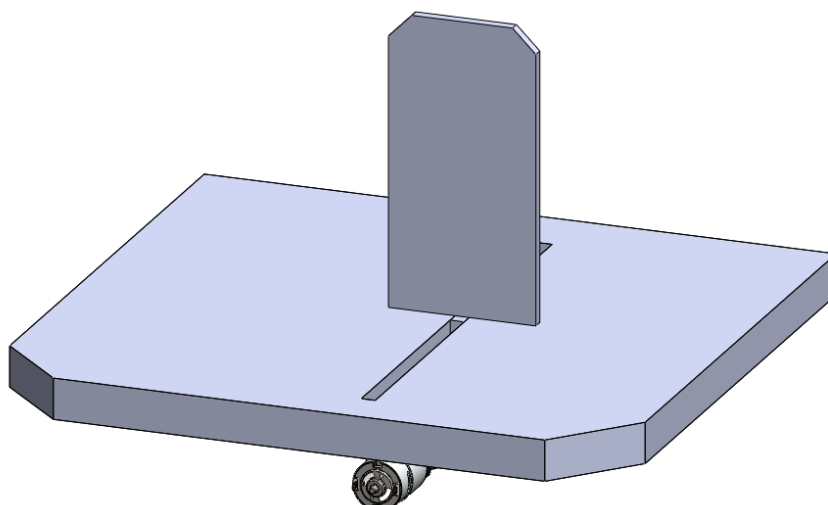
Ajuste frontal. Diseño del acople mecánico que va al motorreductor.
